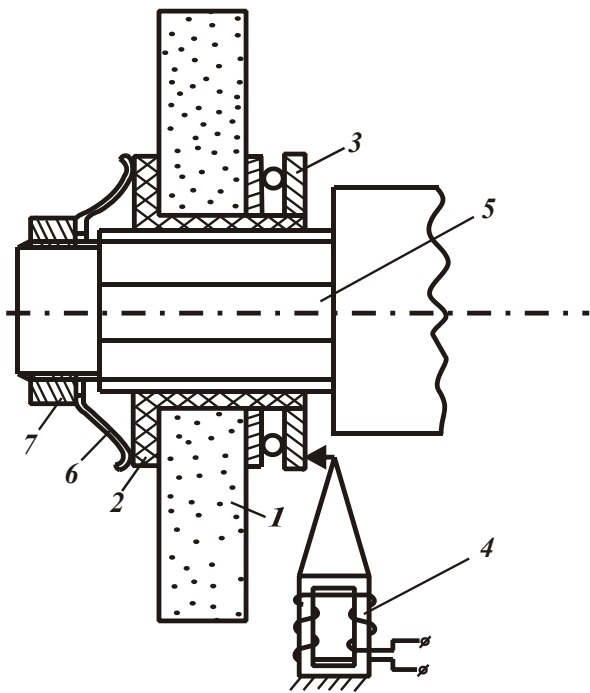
Устройство с осевым перемещением шлифовального круга: 1 – круг; 2 – шлицевая втулка; 3 – подшипник; 4 – магнитострикционная колебательная система; 5 – шлицевый вал; 6 – пружина; 7 – гайка.
